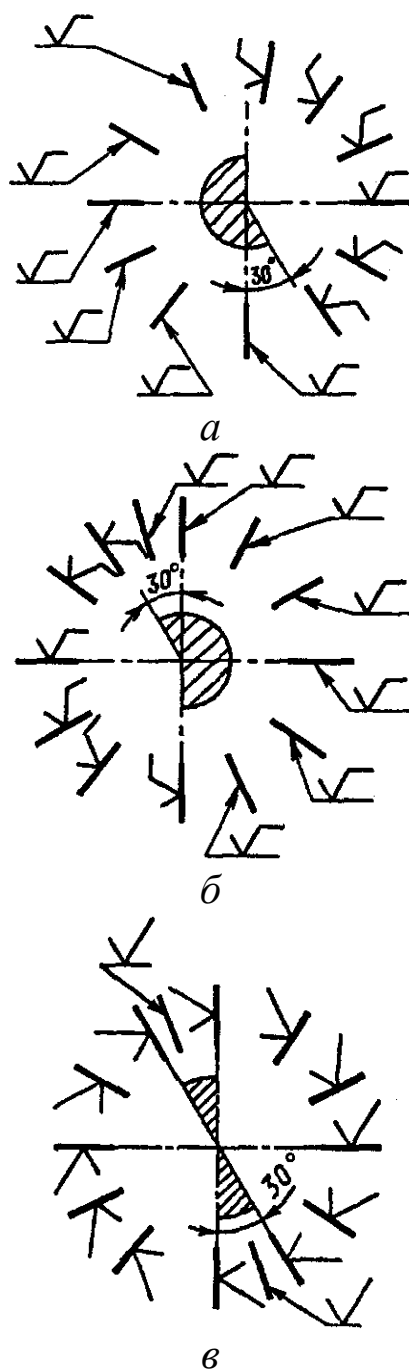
Схема расположения знаков шероховатости поверхности
